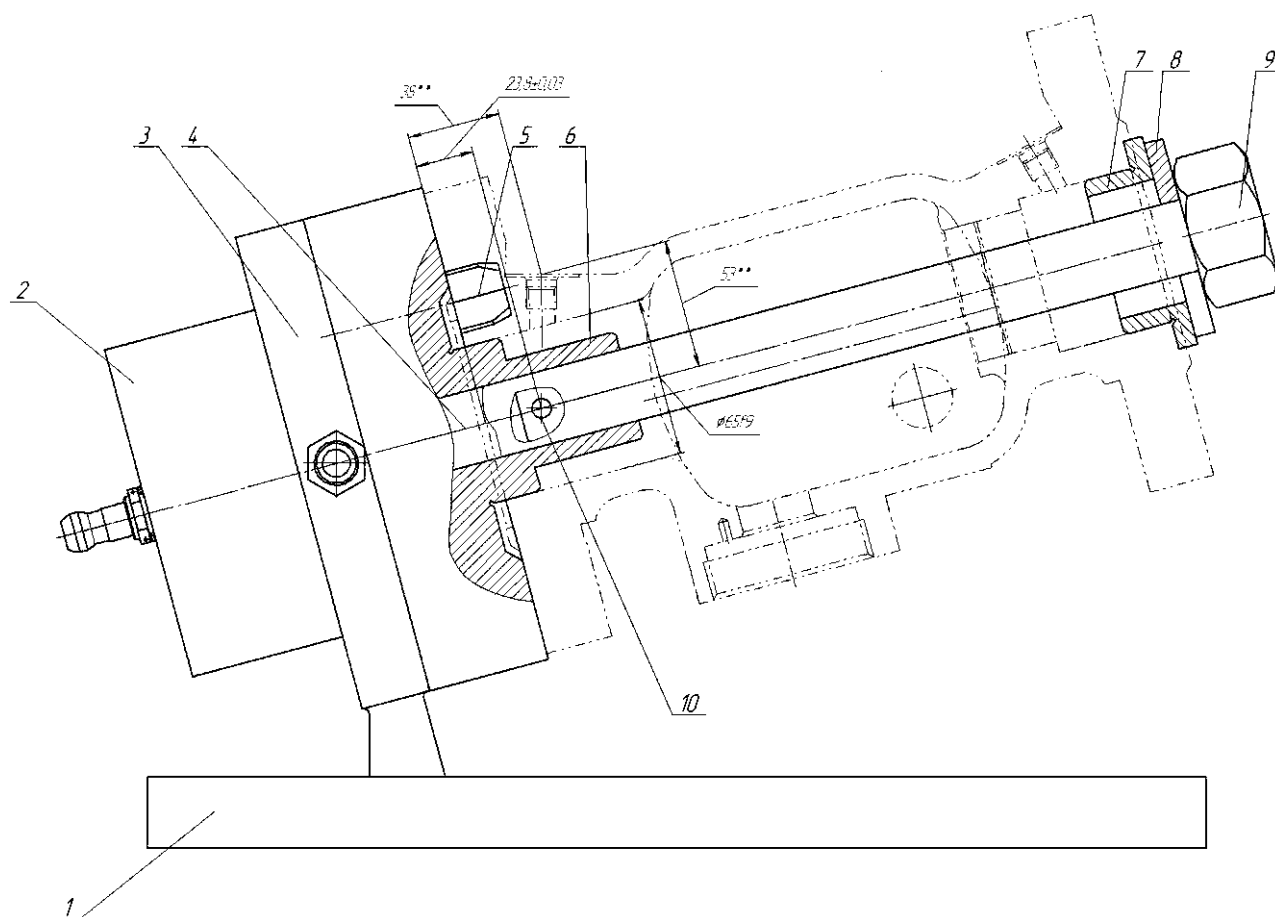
Схема приспособления: 1 – плита приспособления; 2 – пневмопривод; 3 – корпус; 4 – шток; 5 – установочный палец; 6 – база; 7 – центрирующая втулка; 8 – быстросъемная шайба; 9 – гайка; 10 – отверстие для обкатки и выставки инструмента.
